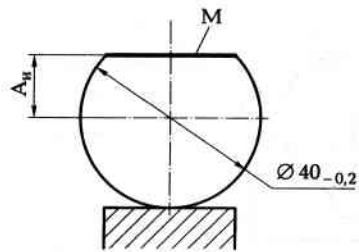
Схема установки заготовки на плоский установочный элемент при фрезеровании плоскости
